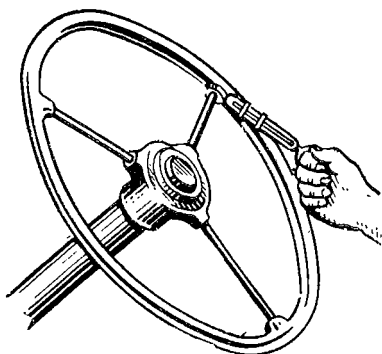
Проверка динамометром усилия поворота рулевого колеса
